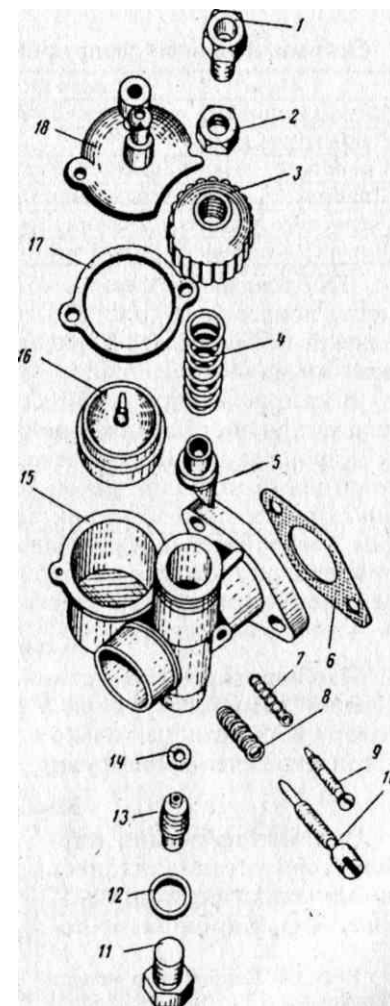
Детали карбюратора К35: 1 - направляющая троса; 2 - гайка М6; 3 - крышка колодца дросселя; 4 - пружина; 5 - дроссель; 6 - прокладка; 7 - пружина; 8 - пружина винта холостого хода; 9 - винт упора; 10 - винт холостого хода; 11 - пробка капала обратного клапана; 12 - шайба фибровая; 13 - жиклер; 14 - шайба фибровая; 15 - корпус карбюратора; 16 - поплавок; 17 - прокладка; 18 - крышка поплавковой камеры в сборе
